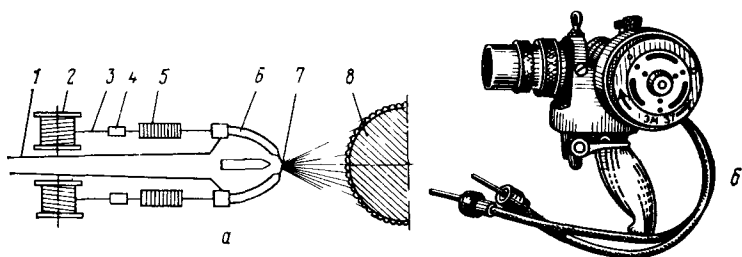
Схема работы (а) и общий вид (б) электродугового металлизатора: 1 — корпус, 2 — барабаны с проволокой; 3 — электродная проволока, 4 — выпрямители; 5 — подаватели, 6 — направляющие проволоки; 7 — воздушный распылитель, 8 — наплавляемая деталь
